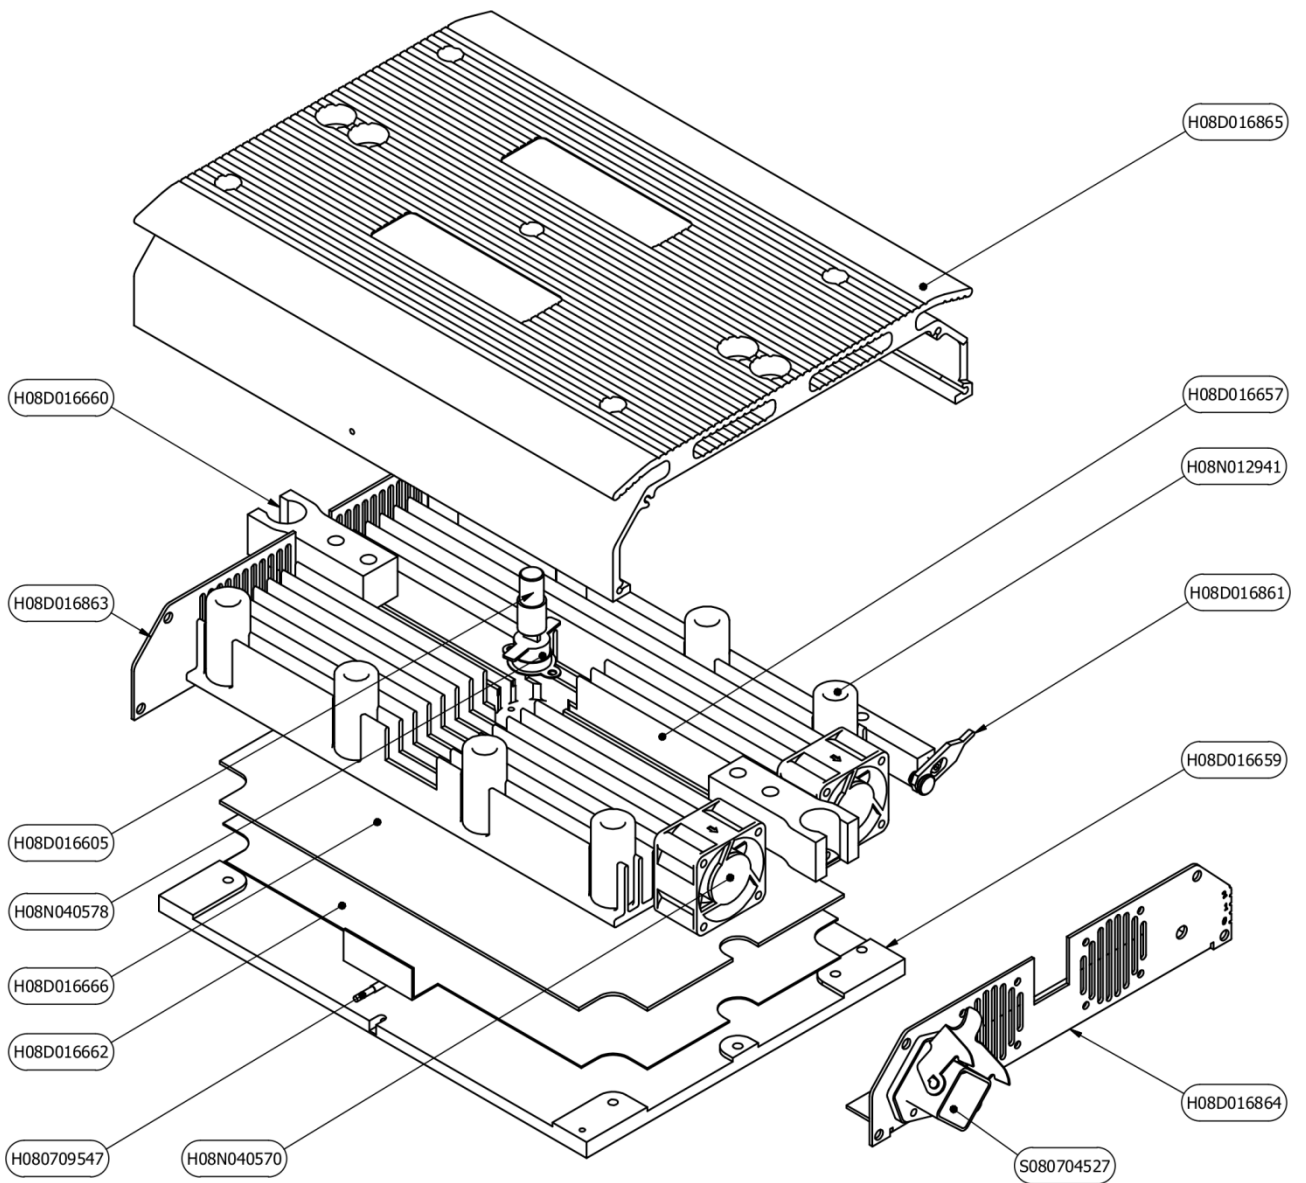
H08D016656 Assemblage de plaque chauffante supérieure PML-200
